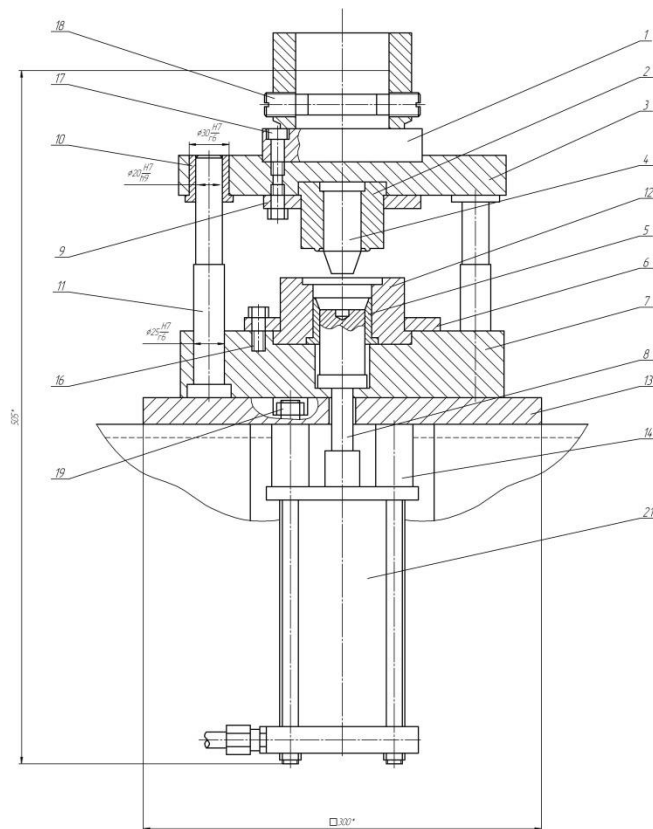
Приспособление для восстановления тарелок клапанных пружин
